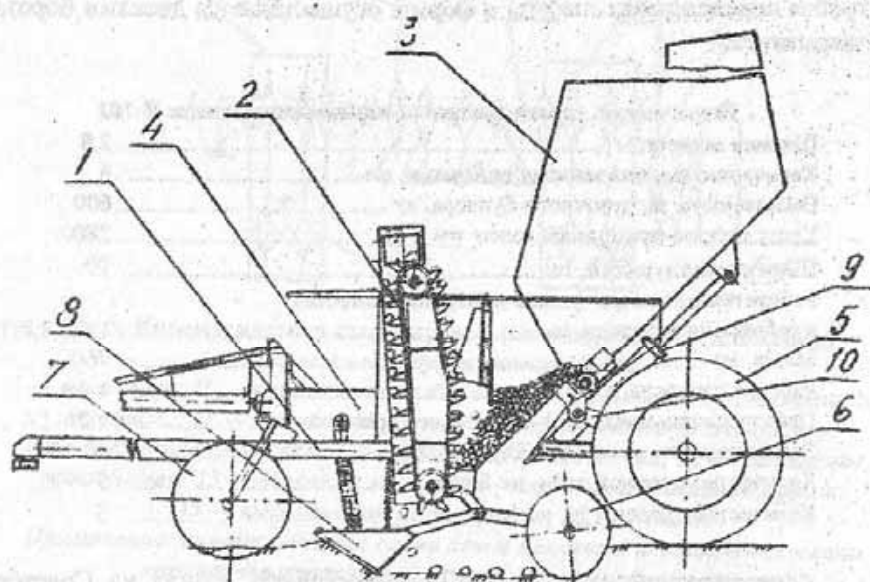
Конструктивно-технологическая схема картофлесажалки Л-207: 1 — рама с прицепом; 2 — высаживающий аппарат; 3 — загрузочный бункер; 4 — туковысевающее оборудование; 5 — ходовое колесо; 6 — бороздозакрыва-тель; 7 — опорное колесо; 8 — сошник; 9 — гидроцилиндр подъема бункера; 10 — рамка полуоси ходового колеса.
